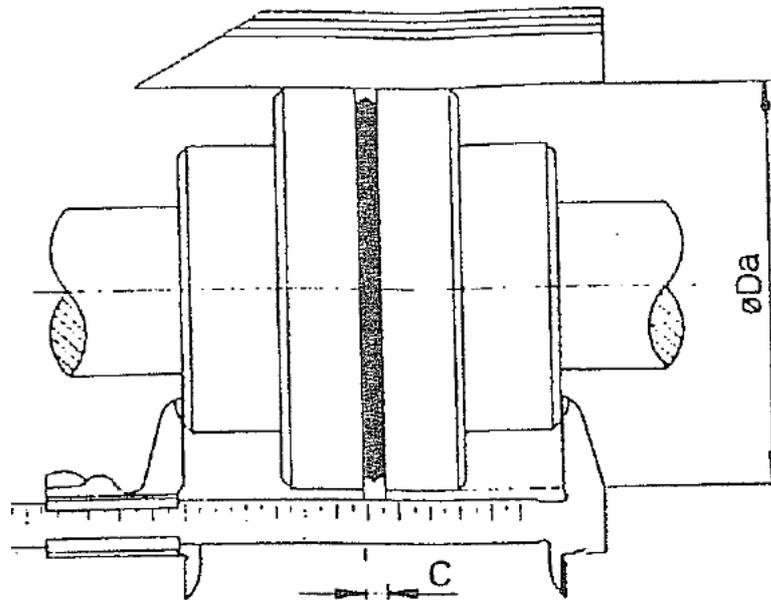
Ausrichtung der Kupplung zwischen Getriebemotor und Drehkolbenpumpe
